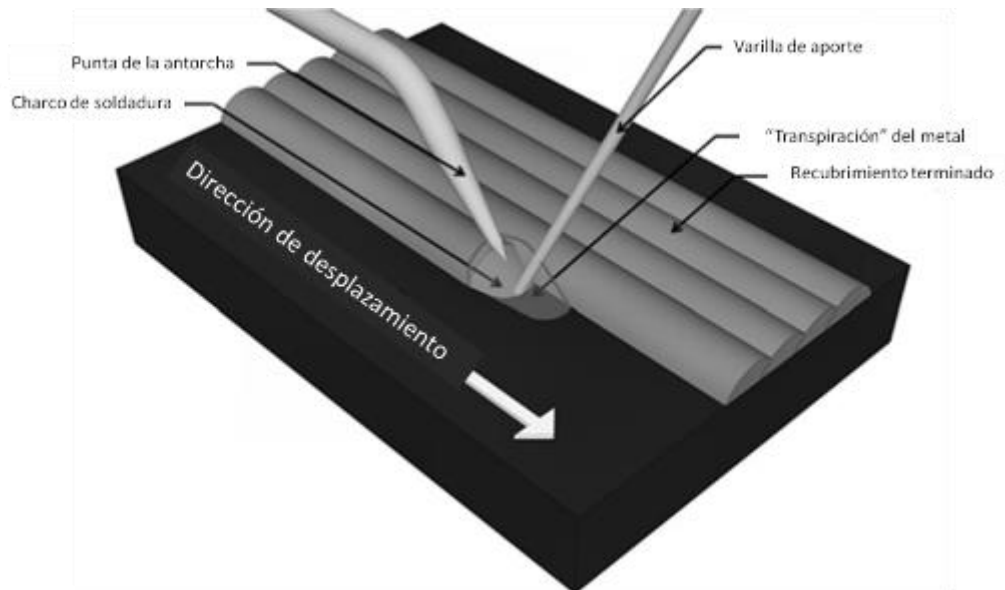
Esquema del proceso de soldadura fuerte con flama de Oxy-acetileno (3).
